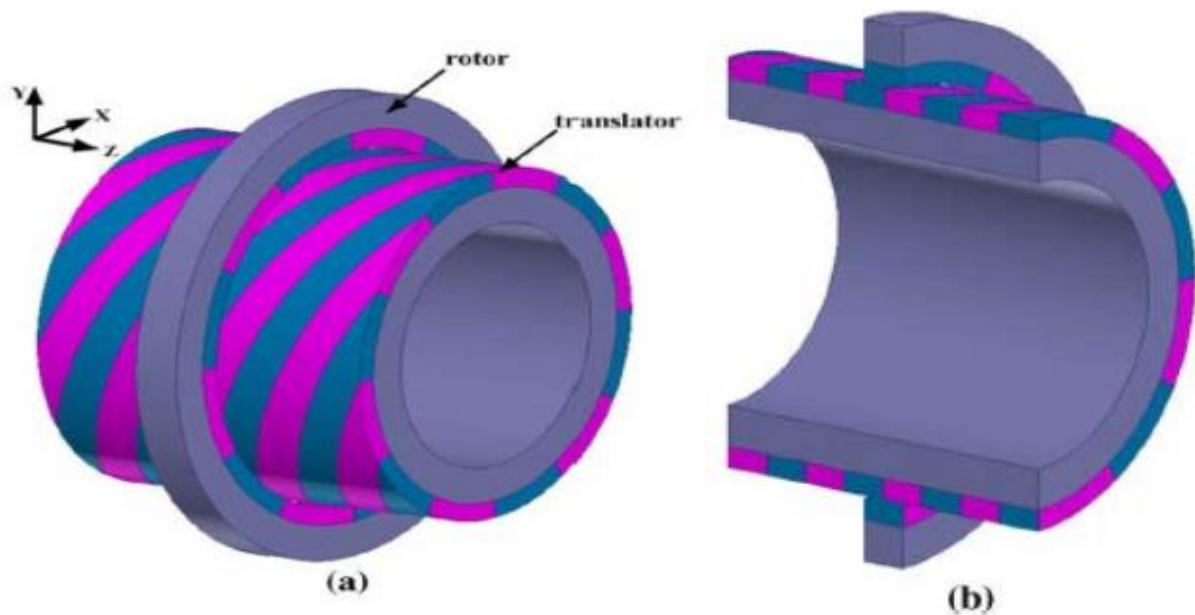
(a) vue en 3D et (b) vue en coupe d'un TROMAG à 12 pôles [PFT13]
